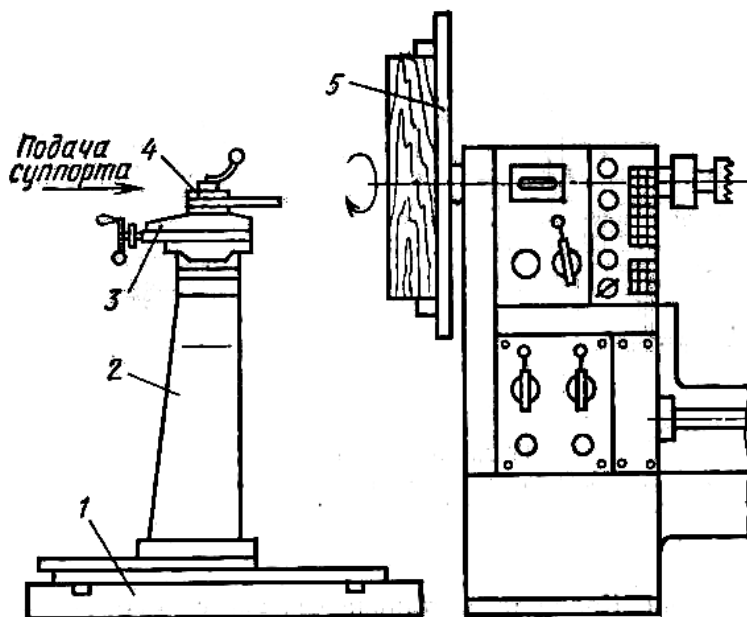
Токарный станок с механической подачей суппорта ТС40:
